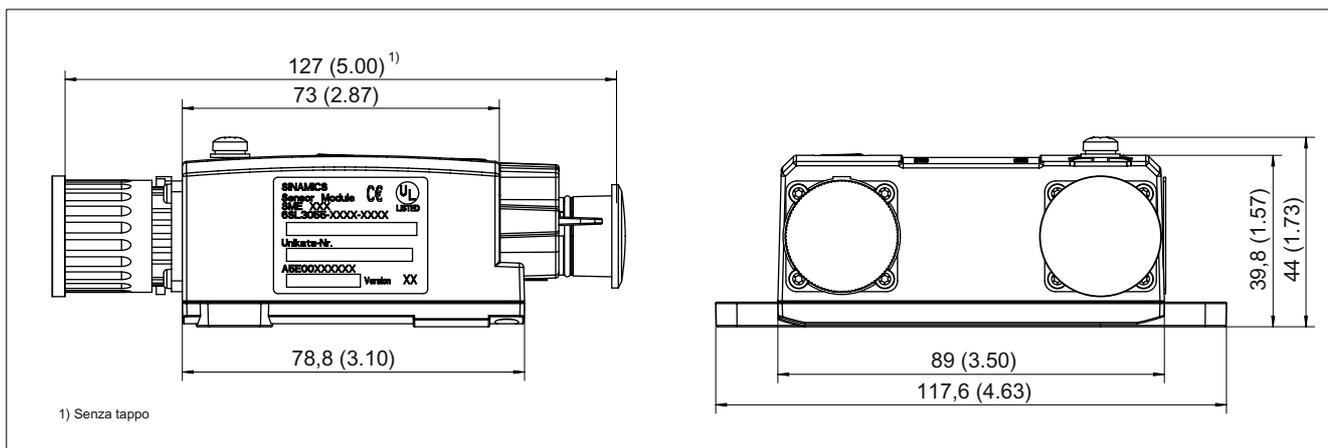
Disegno quotato Sensor Module External SME120, tutte le misure in mm e (inch), N. di ordinazione 6SL3055-0AA00-5JA0
